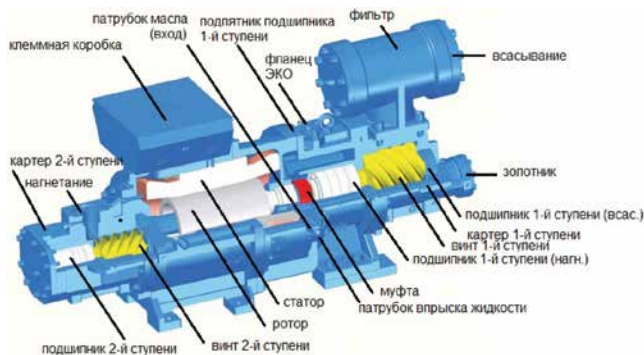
Винтовой двухступенчатый холодильный компрессор SRT
